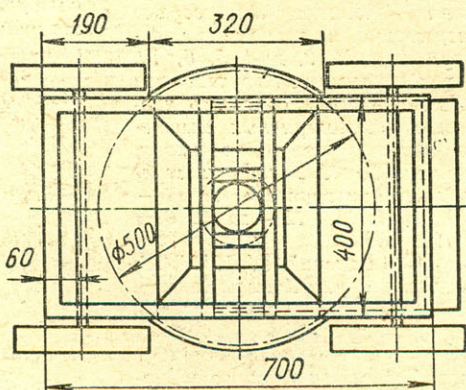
Габаритные размеры и компоновка косилки с электродвигателем.
